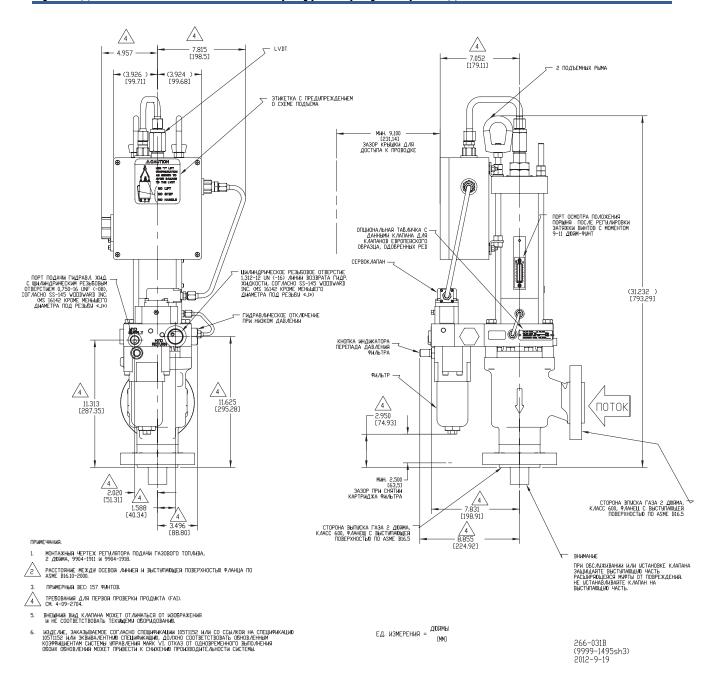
Габаритный чертеж регулятора SonicFlo (2 дюйма, класс 600)
